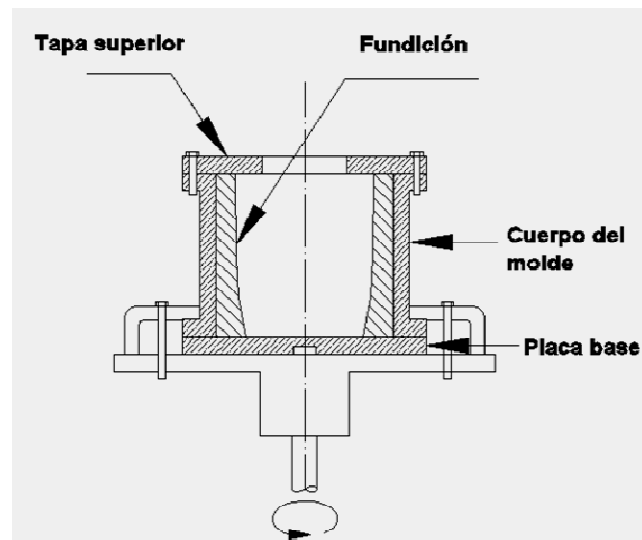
ESQUEMA DE LAS PARTES DE UN MOLDE PARA FUNDICIÓN CENTRÍFUGA.
